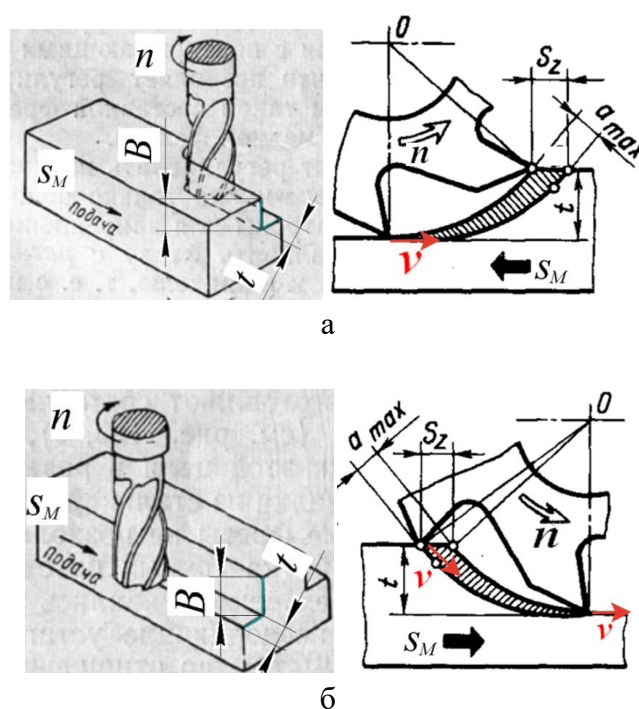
Схема направления подачи s_m (мм/мин) заготовки, скорости вращения фрезы n (об/мин) и скорости резания v (м/мин) при встречном фрезеровании (а) и при попутном фрезеровании (б)
